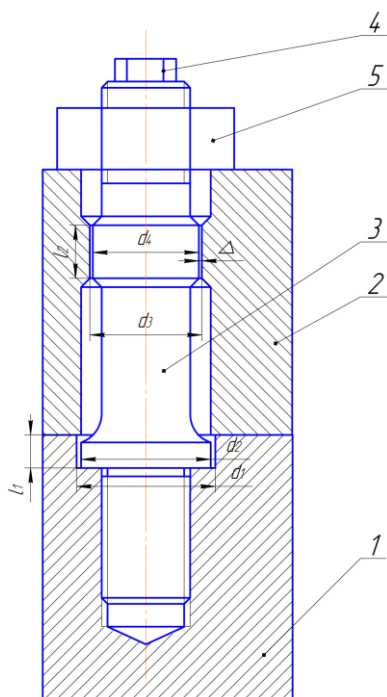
Конструкция резьбового соединения деталей сельхозмашин повышенной прочности
